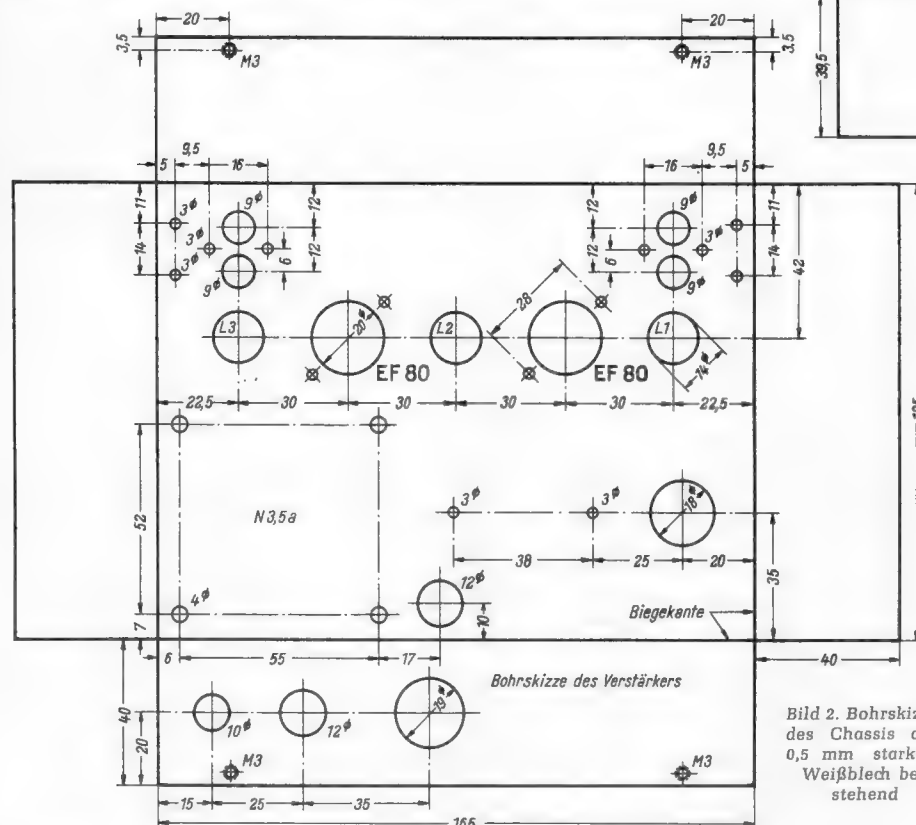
Bohrskizze des Chassis aus 0,5 mm starkem Weißblech bestehend
